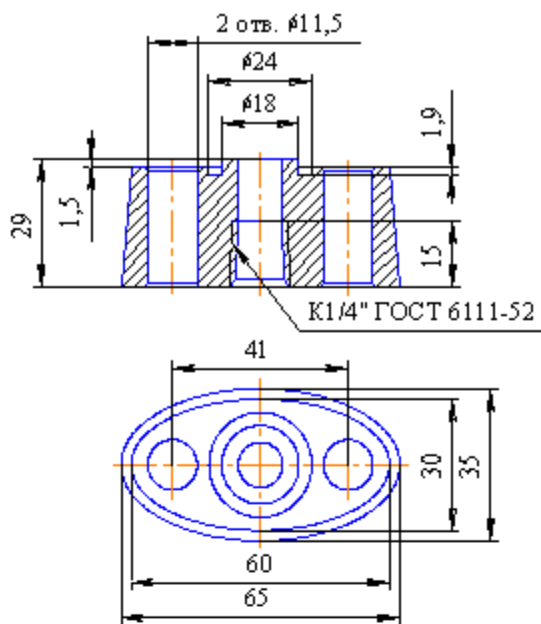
КМЧ: овальный фланец с резьбой K1/4"
